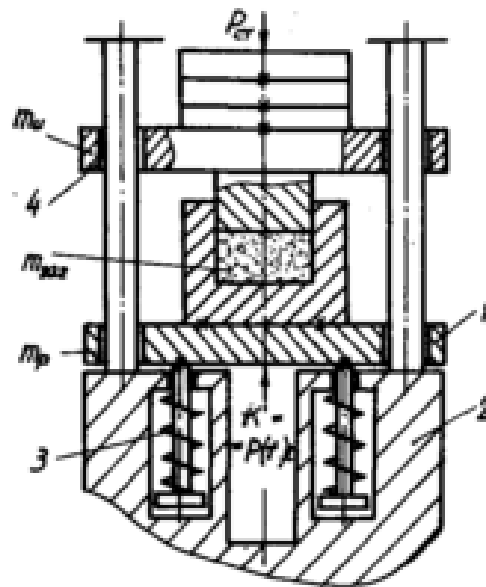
Схема інерційного навантаження заготовки при жорстких (знизу) та пружних (зверху), зв'язках, що обмежують
